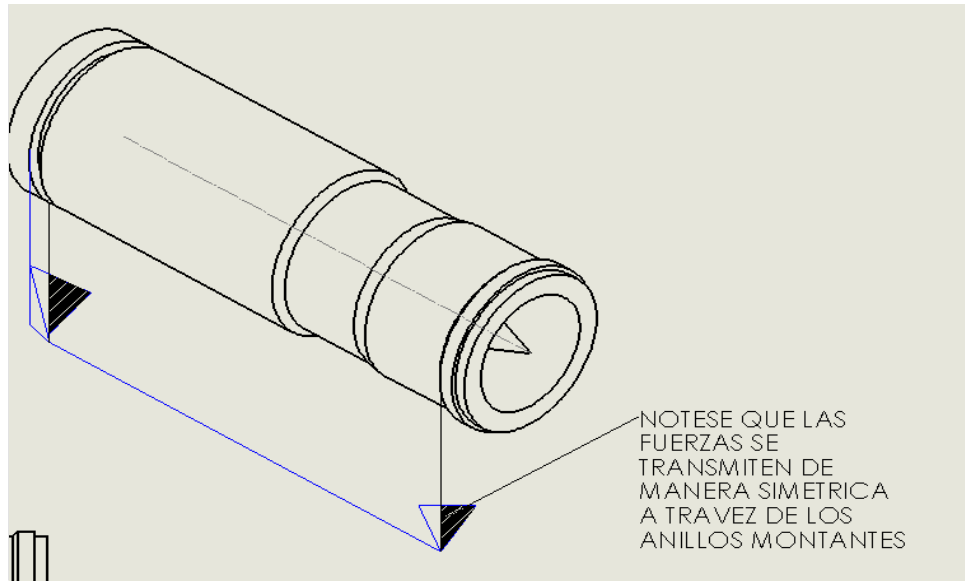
Detalle de la simetría de fuerzas aplicadas por el motor
